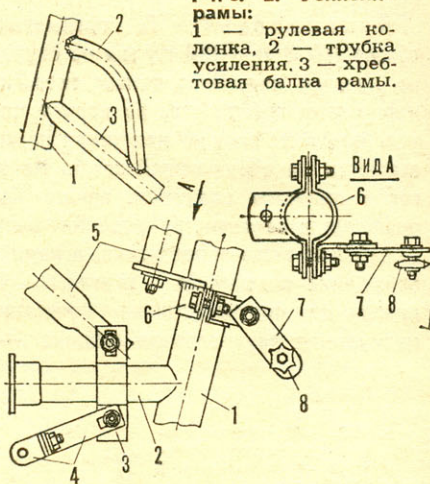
Крепление двигателя: 1 — подседельная стойка рамы, 2 — хребтовая балка рамы, 3 — хомут, 4 — кронштейн глушителя, 5 — трубки (кронштейн двигателя), 6 — хомут, 7 — кронштейн звездочки натяжения, 8 — звездочка натяжения.
